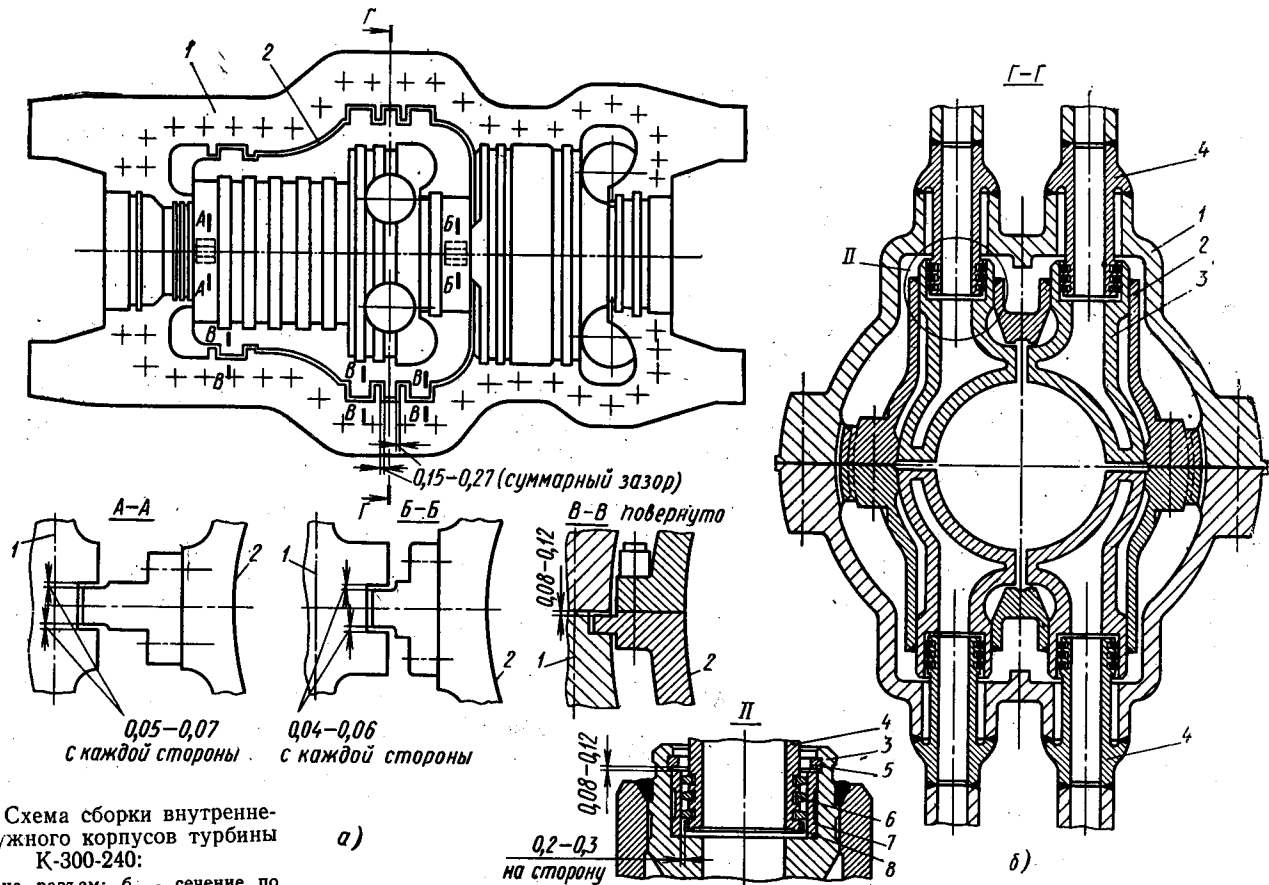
Схема сборки внутреннего и наружного корпусов турбины К-300-240:
